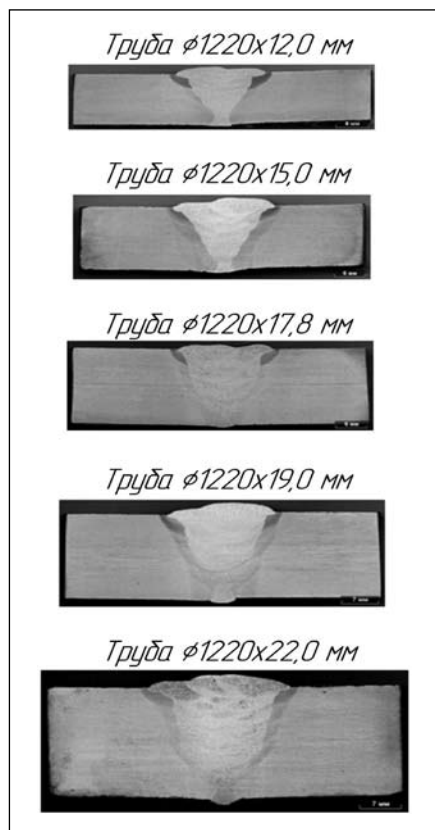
Макрошлифы из соединений, выполненных автоматической сваркой самозащитной порошковой проволокой
